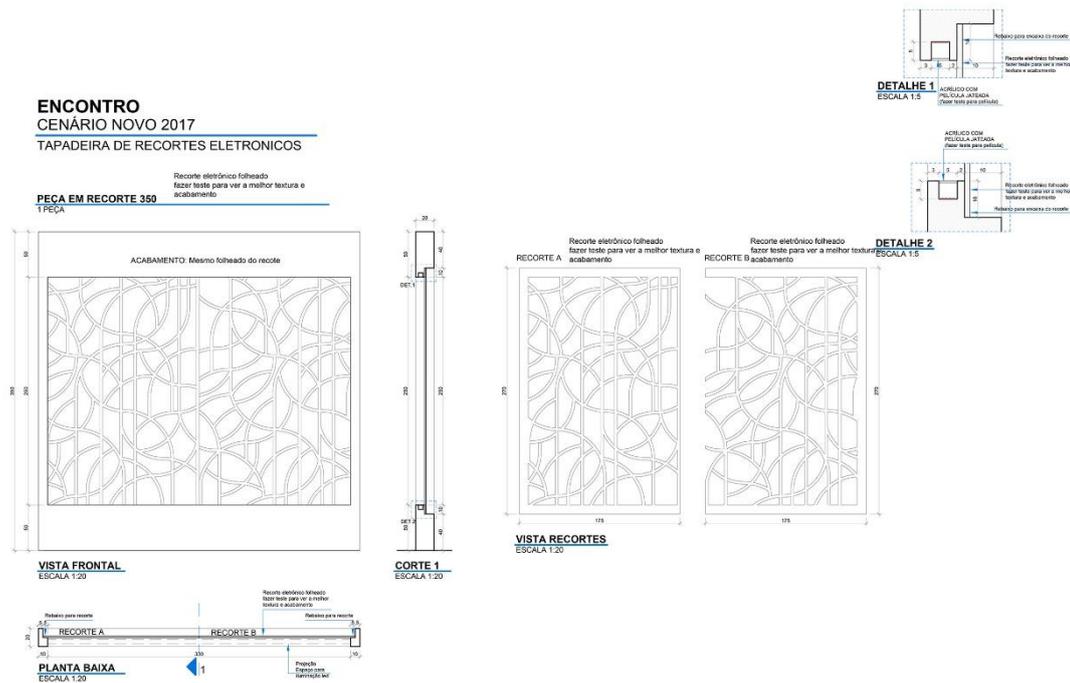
Desenho técnico – detalhe da tapadeira com recorte eletrônico. Fonte: arquivo pessoal.
